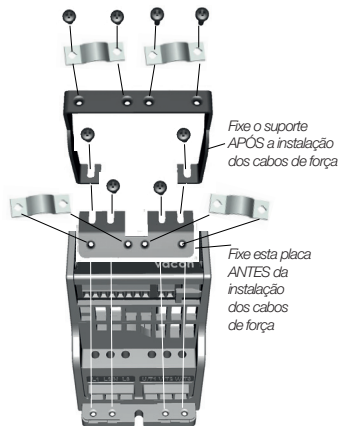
Instalação da placa PE e suporte a cabo API, MI1 - MI3
